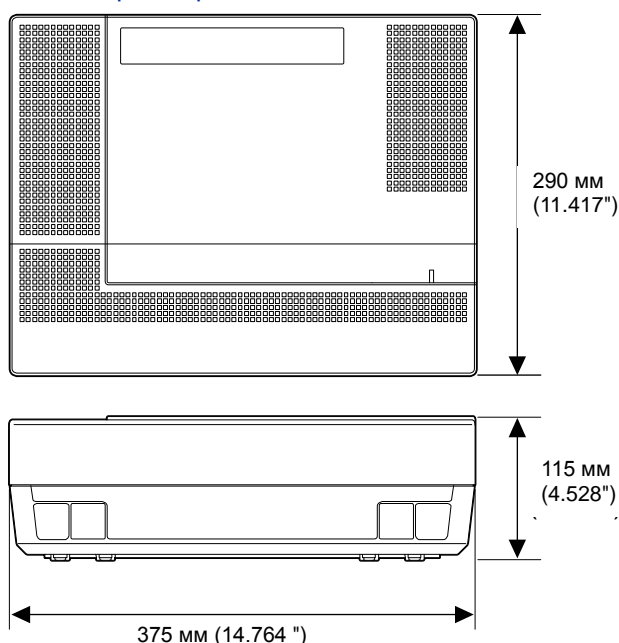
Габаритные размеры главной и расширяемой мини-АТС
